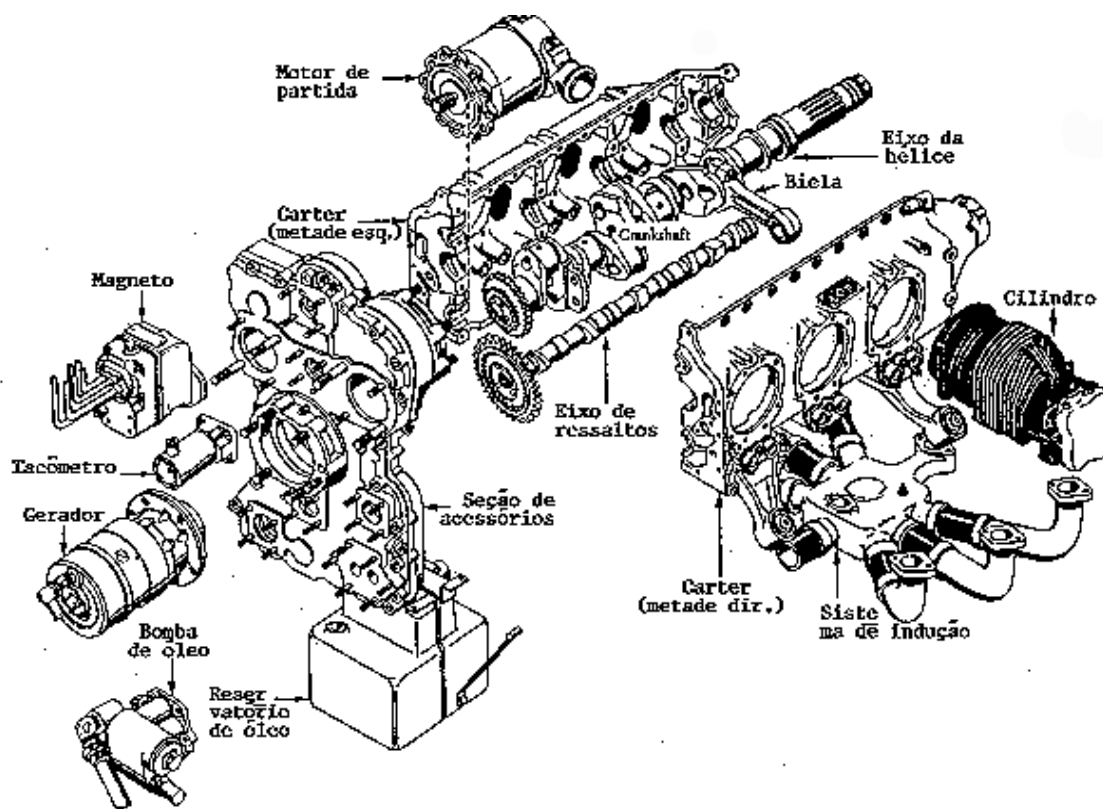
Vista explodida de um típico motor de cilindros opostos e seus componentes.
